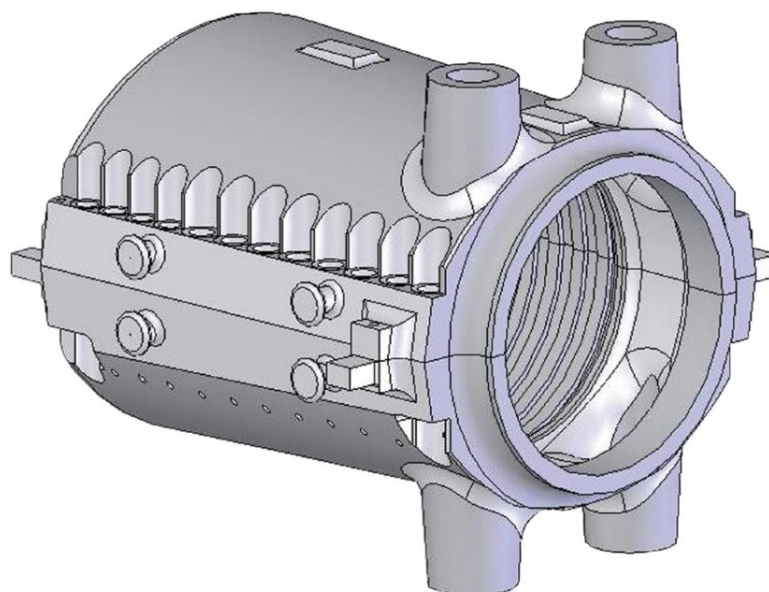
Внутренний корпус цилиндра турбины Т-63/76-8,8
